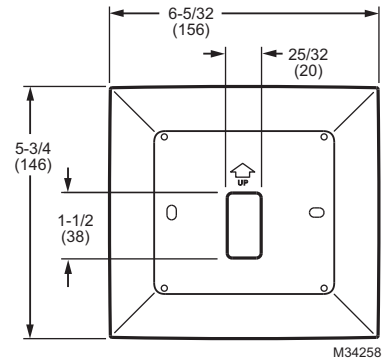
Dimensions de la plaque de recouvrement du VisionPRO en po (mm)
